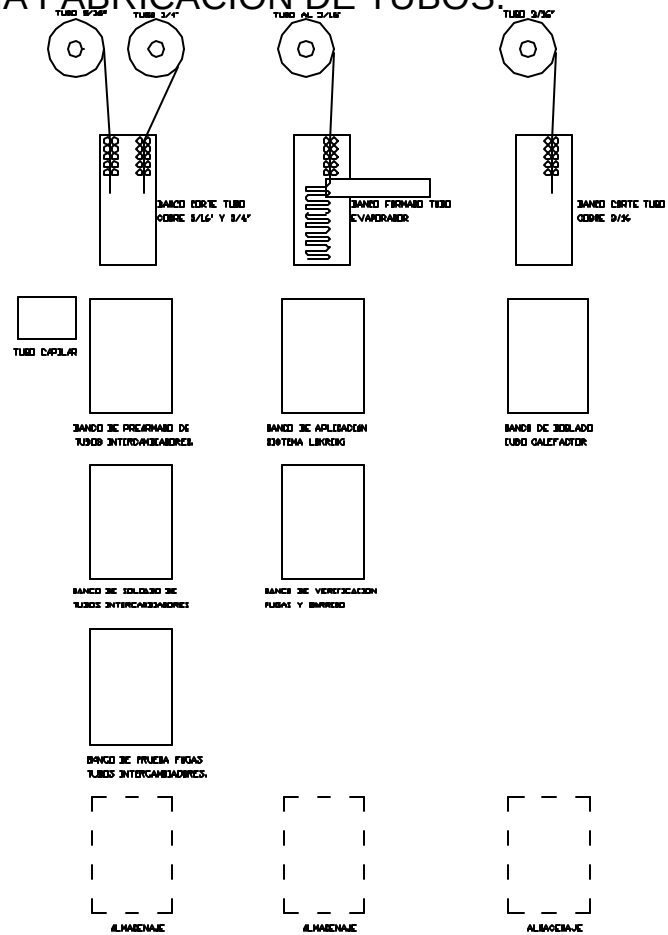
, Nuevo Layout esquemático de la zona de proceso y soldadura
